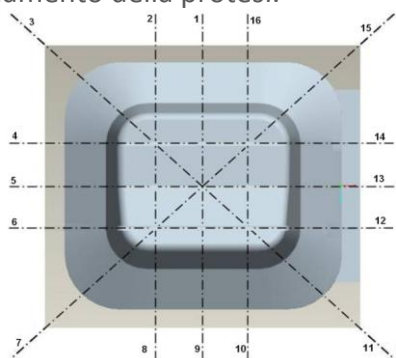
PIANI DI SEZIONAMENTO DELL'ELEMENTO MOLARE
